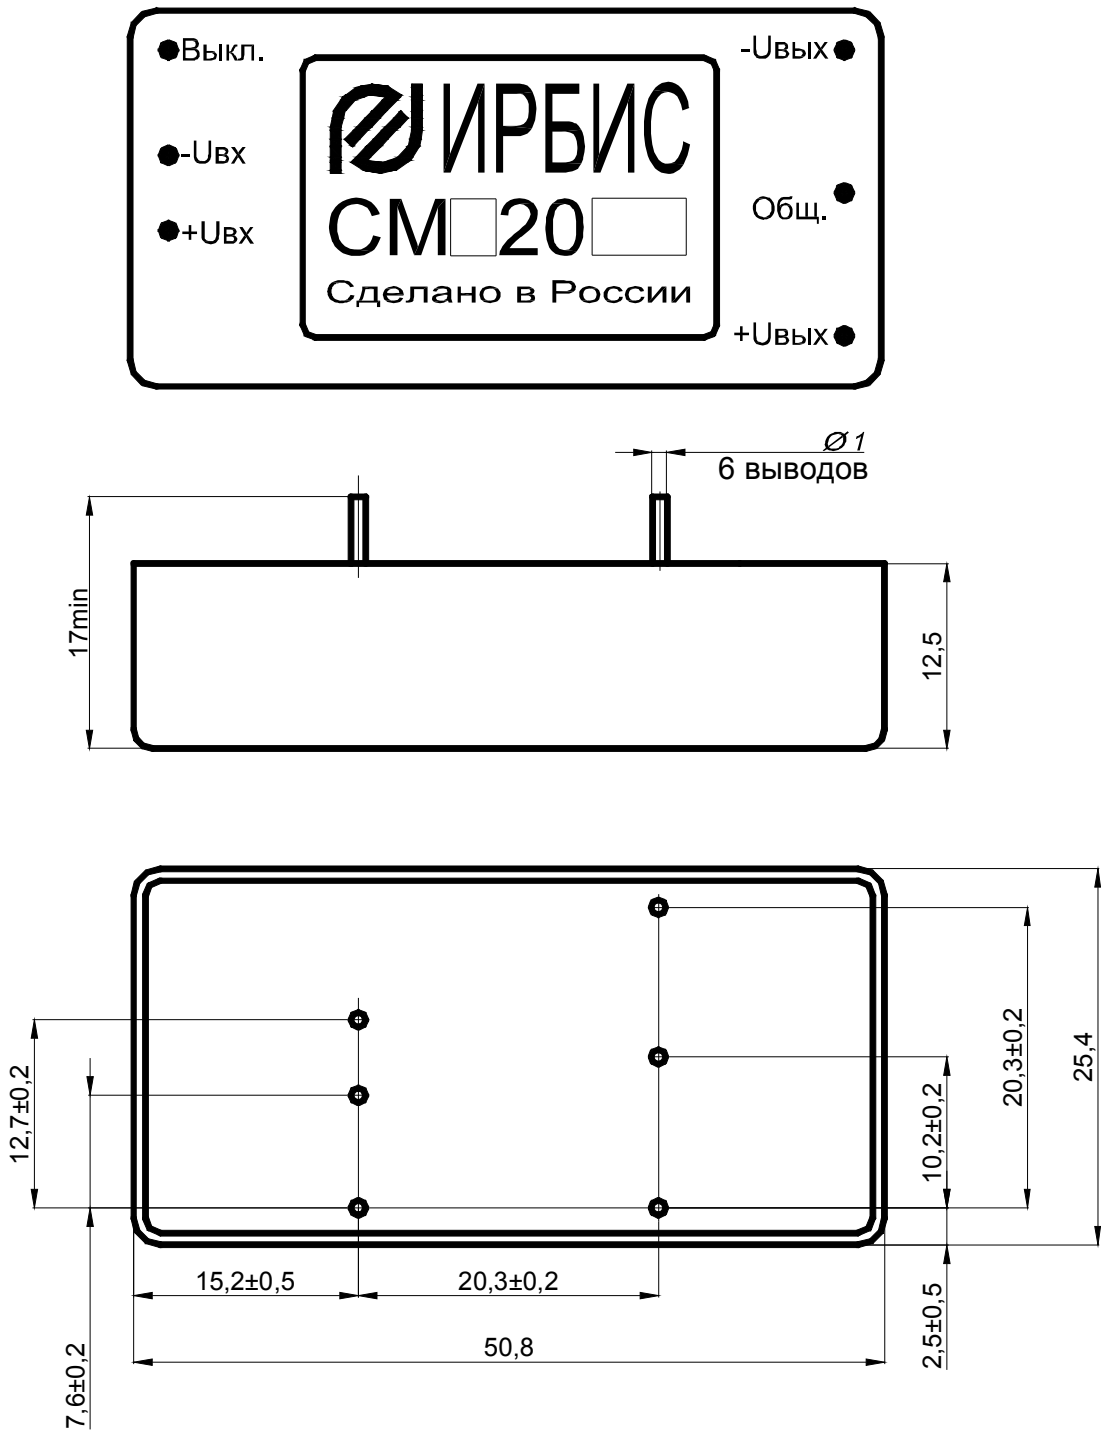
Габаритный чертеж модулей СМА(В,Е,Т)20
